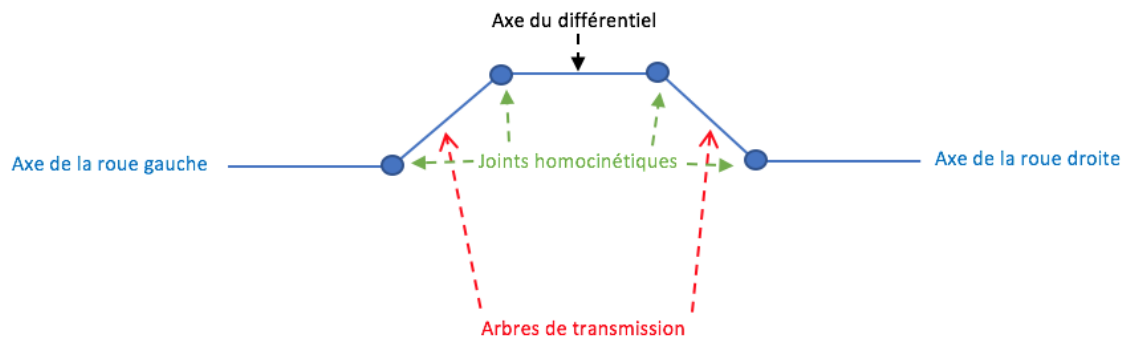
Schéma explicatif de la géométrie des joints, vue de derrière
